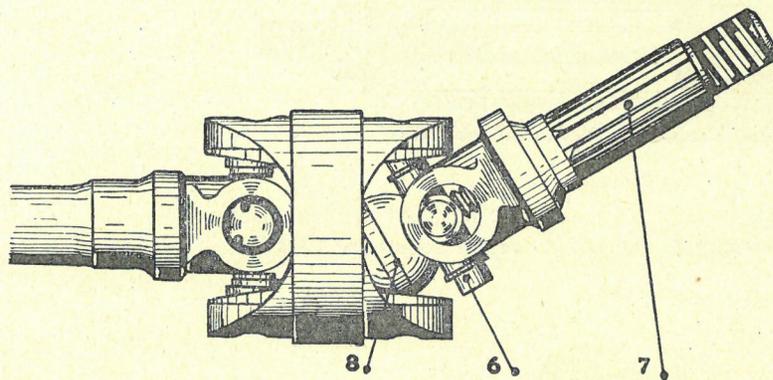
DÉMONTAGE DE LA MACHOIRE DOUBLE
